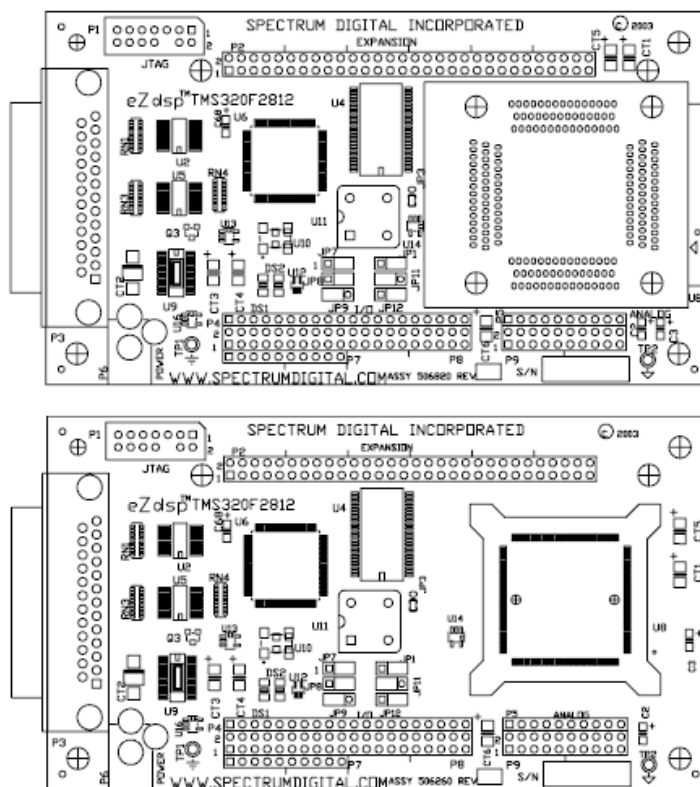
Versione (socketed e unsocketed) della eZdsp™ F2812 [Dat¹]
